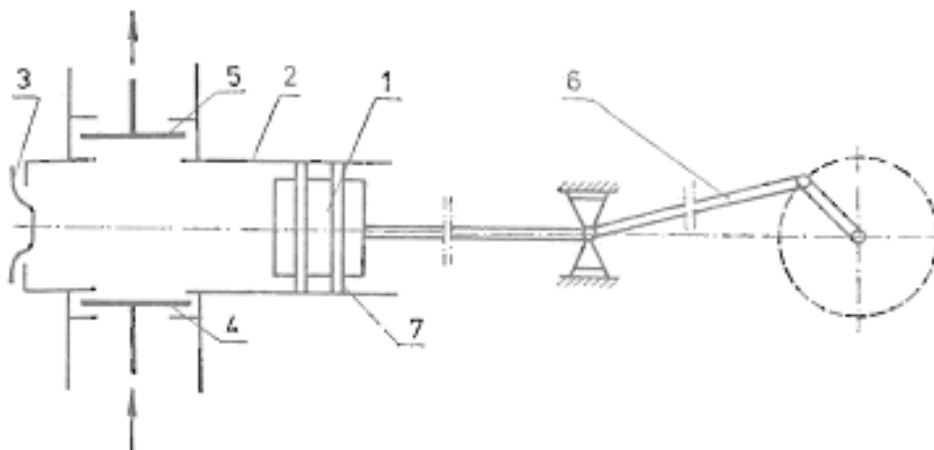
Schema pompei cu piston cu simplă acțiune: 1-piston; 2-cilindru; 3-capacul cilindrului; 4-supapa de aspirație; 5-supapa de refulare; 6-mecanism biela-manivela; 7-segment de etanșare.
